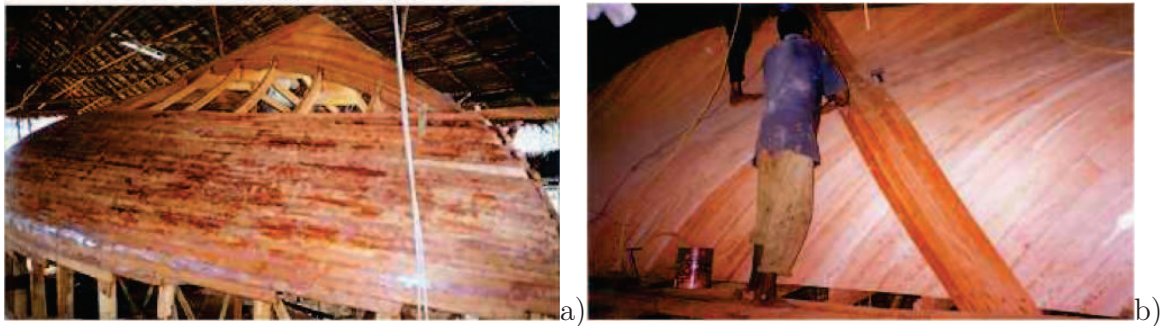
Techniques de fabrication de bateaux bois : a) Strip-planking, b) bois moulé [6]
